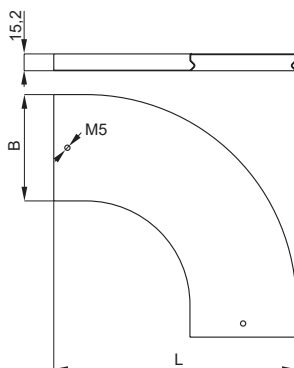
Крышка поворота плавного на 90° /
